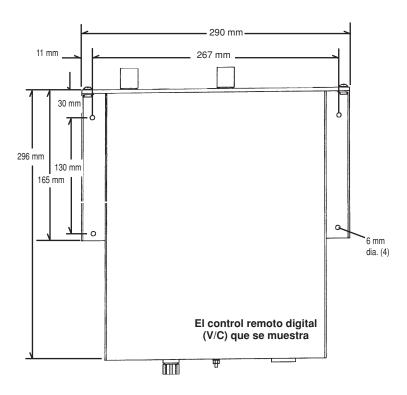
Dimensión de montura – Control remoto digital V/C
